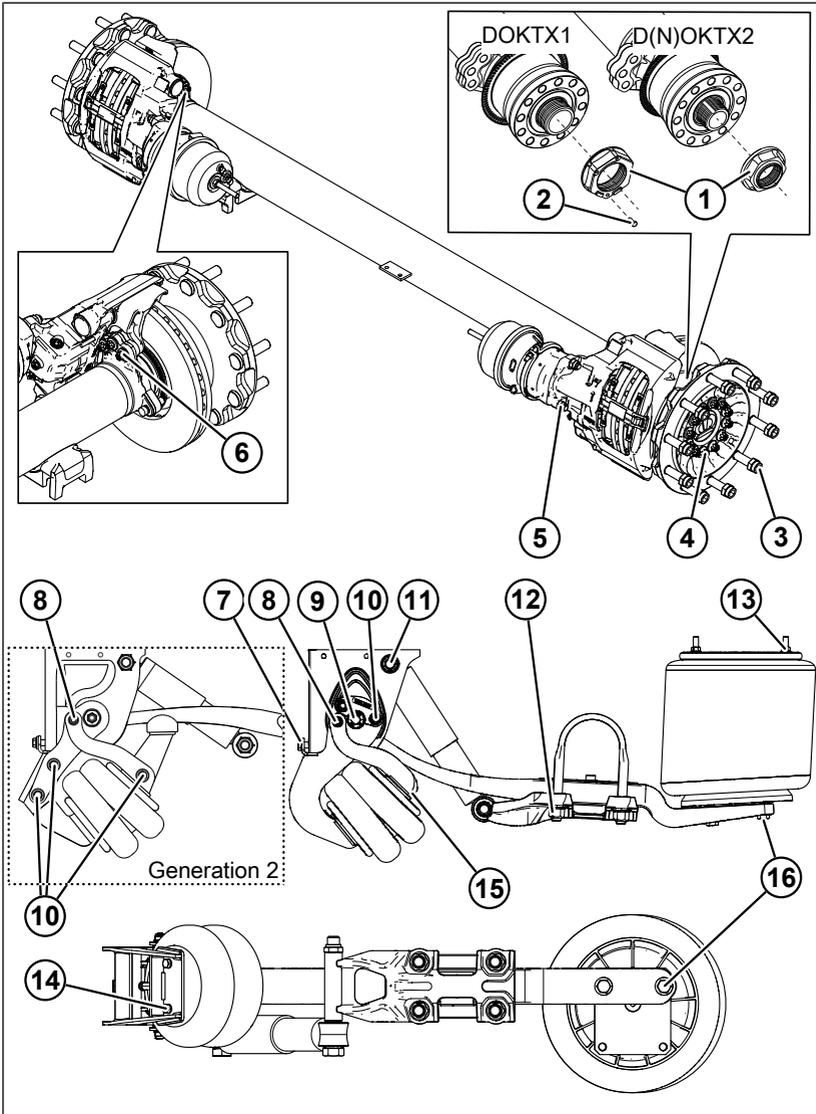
Vue d'ensemble des couples de contrôle et de serrage (bras de suspension pneumatique inférieur)
